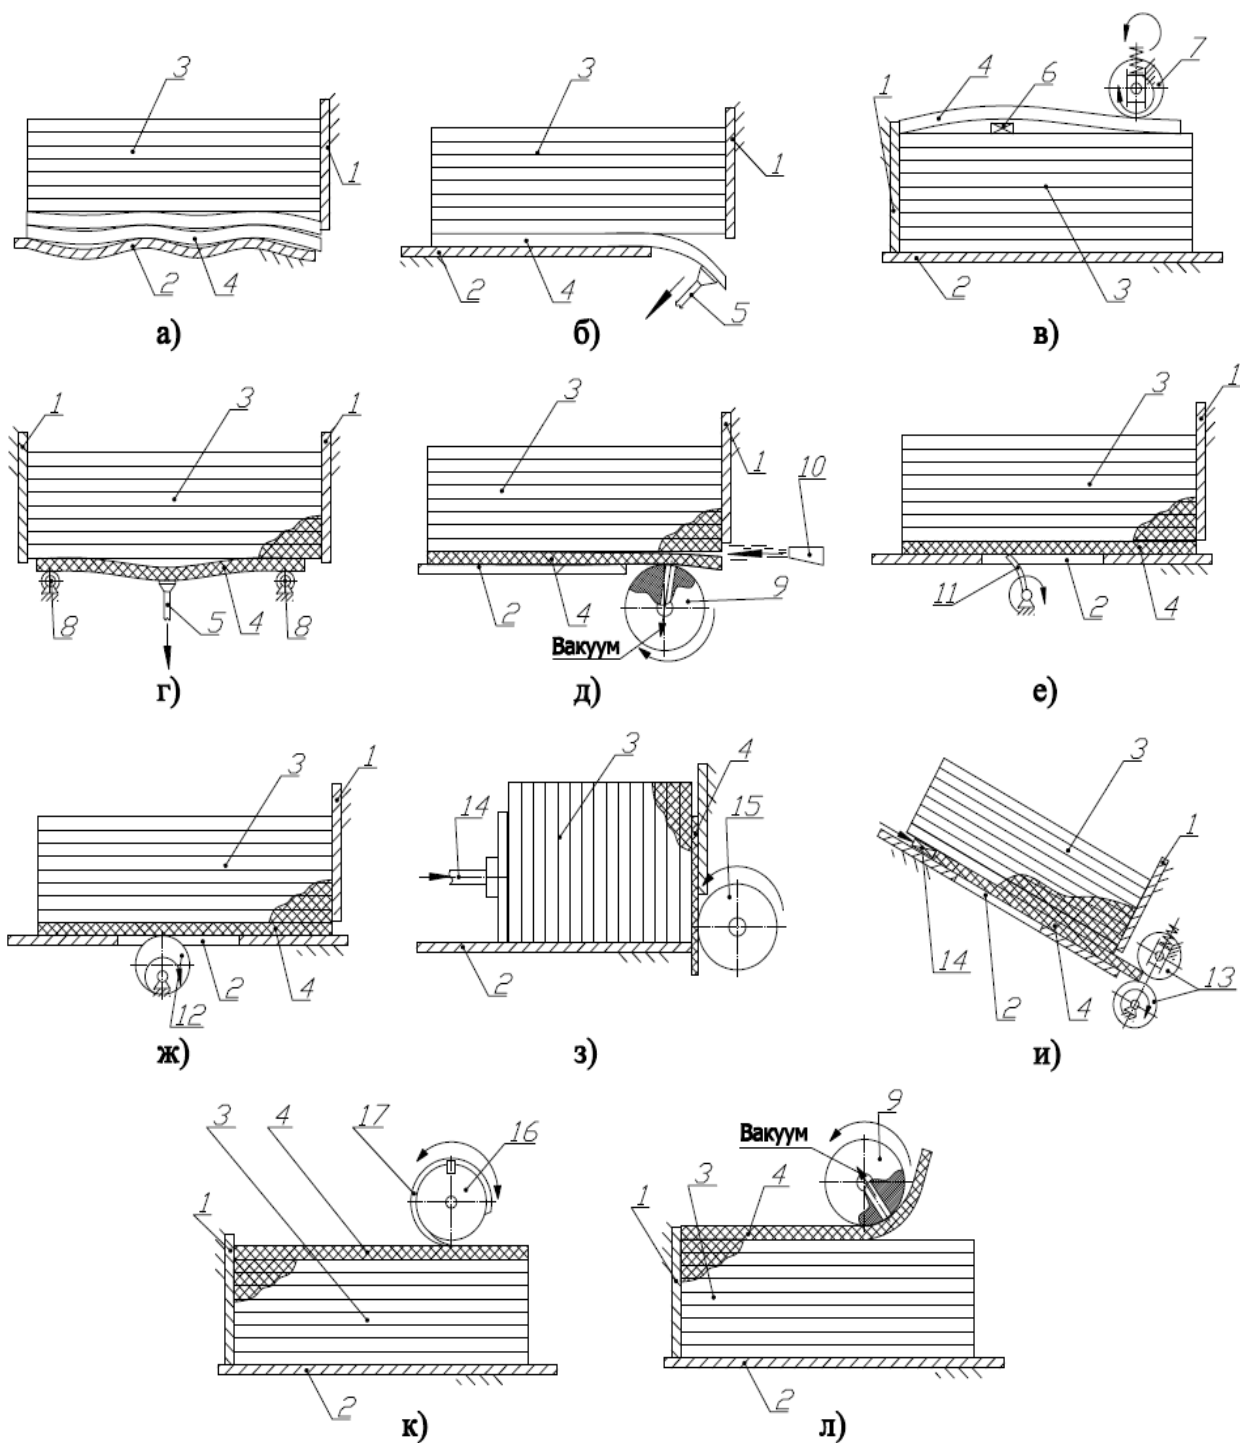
Способи поштучного відокремлення заготовок листового типу: 1-корпус магазину; 2– дно магазину; 3 - стос заготовок; 4 – заготівка, що відокремлюється; 5 - робочий орган; 6 – притискач; 7– валик подачі; 8-опірний валик; 9-валик вакуумний; 10-сопло; 11-гучкий захватний орган; 12- валик-ексентрик; 13- валики; 14-штовхач; 15- валик; 16-валик; 17-голчастий захватний орган
